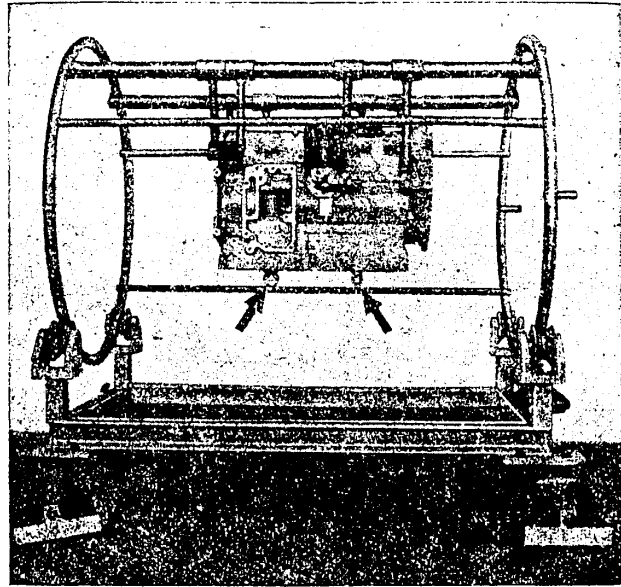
Motor im Montagewagen (180° gedreht), Sicherungsschrauben (Pfeile)
